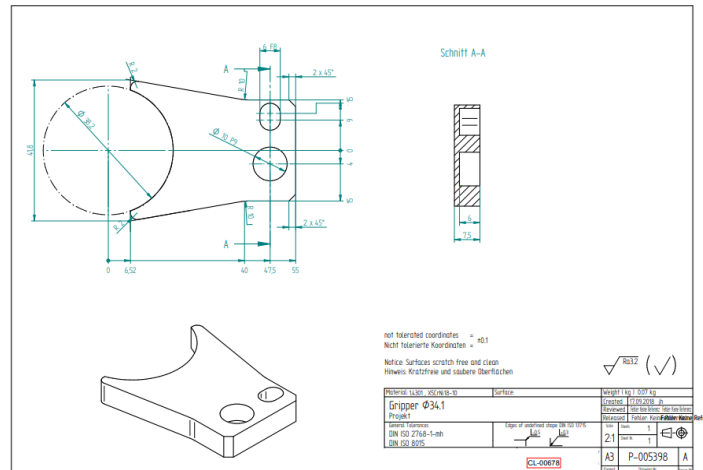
Робоче креслення деталі з технологічними вимогами.
